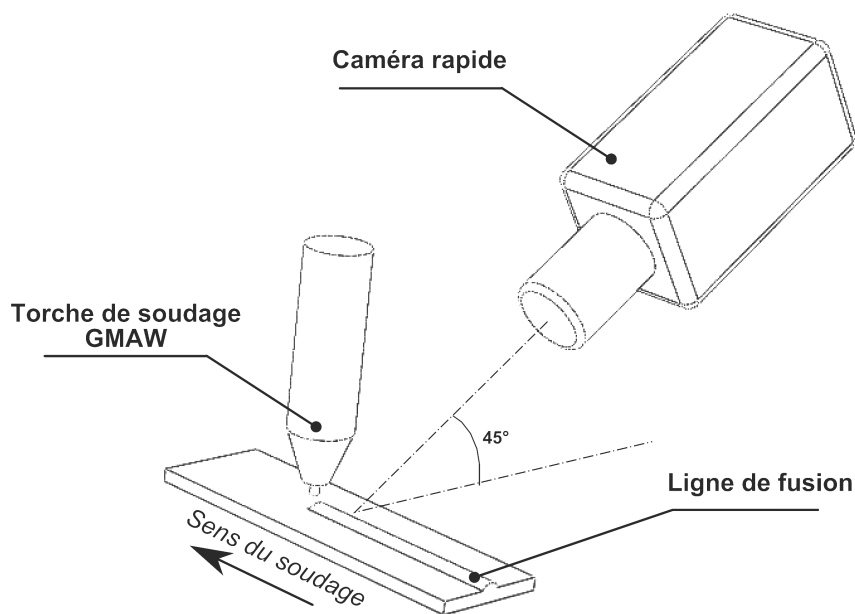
Position de la caméra vis-à-vis de la pièce soudée
